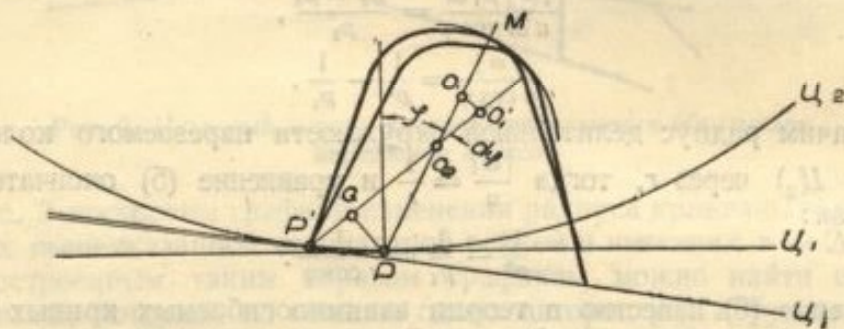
Исходный контур реечного инструмента обкатывает нарезаемое колесо.
